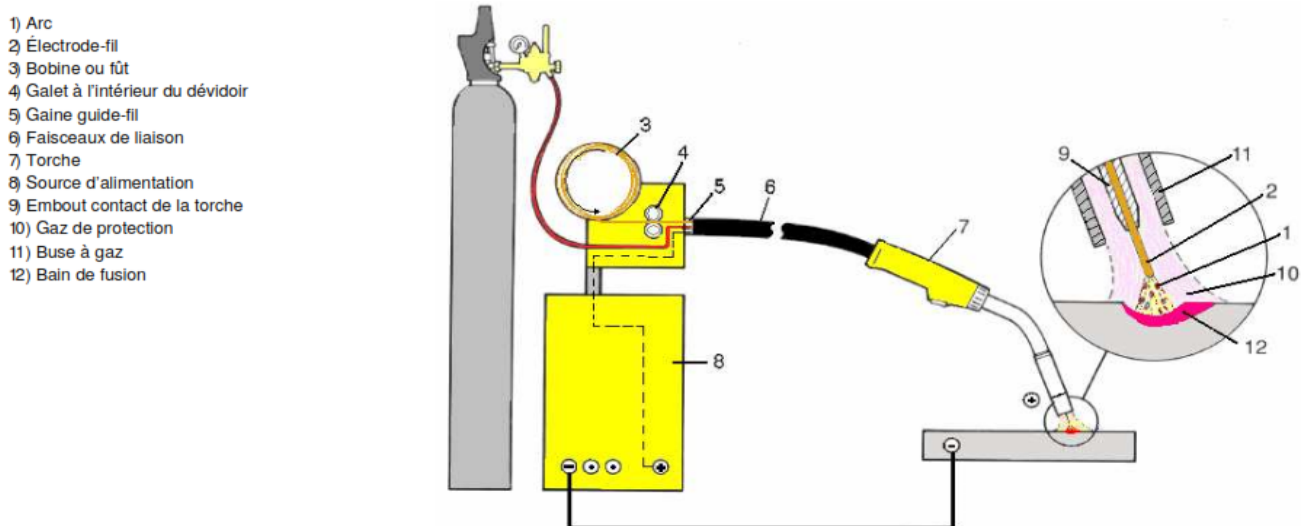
4 : Installation de soudage MIG/MAG [10].
